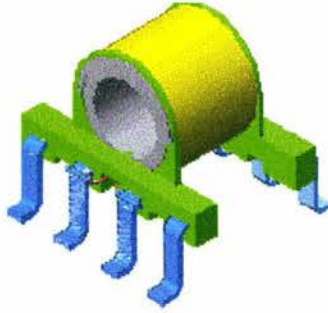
Terminales de la pieza A y puntas del embobinado soldadas (Pieza D). (Cortesía de Midcom Inc.)
